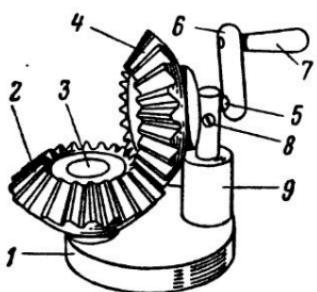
Модель передачи с коническими зубчатыми колесами: 1 — основание; 2 — ведомое колесо; 3 — ось; 4 — ведущее колесо; 5 — вал привода; 6 — рычаг; 7 — ручка; 8 — стопорный винт; 9 — стойка.
